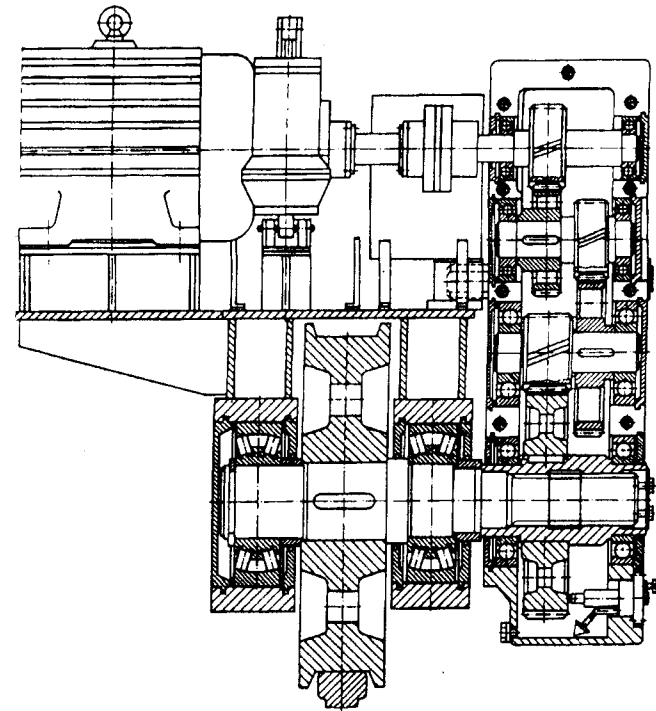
Раздельный привод механизма передвижения с навесным редуктором типа ЦЗВК и электродвигателем на лапах
